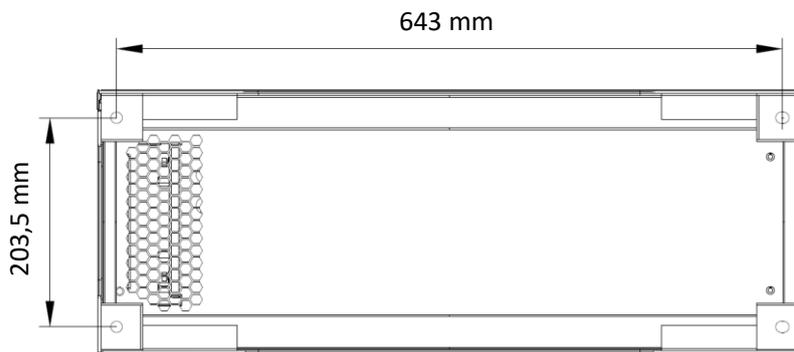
Bemaßung Bohrlöcher für Bodenbefestigung
